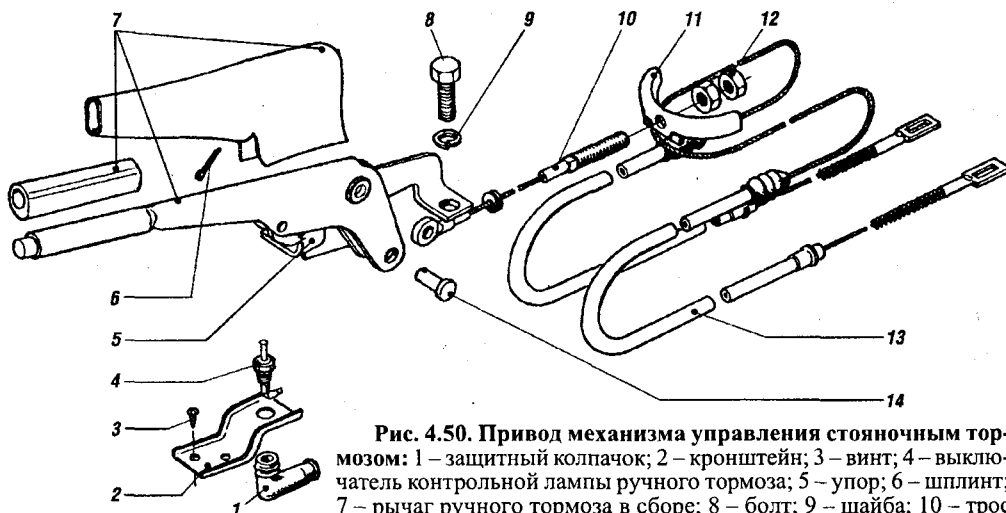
Привод механизма управления стояночным тормозом: 1 – защитный колпачок; 2 – кронштейн; 3 – винт; 4 – выключатель контрольной лампы ручного тормоза; 5 – упор; 6 – шплинт; 7 – рычаг ручного тормоза в сборе; 8 – болт; 9 – шайба; 10 – трос передний в сборе; 11 – уравниватель тормозов; 12 – гайка; 13 – трос ручного тормоза в сборе; 14 – палец
